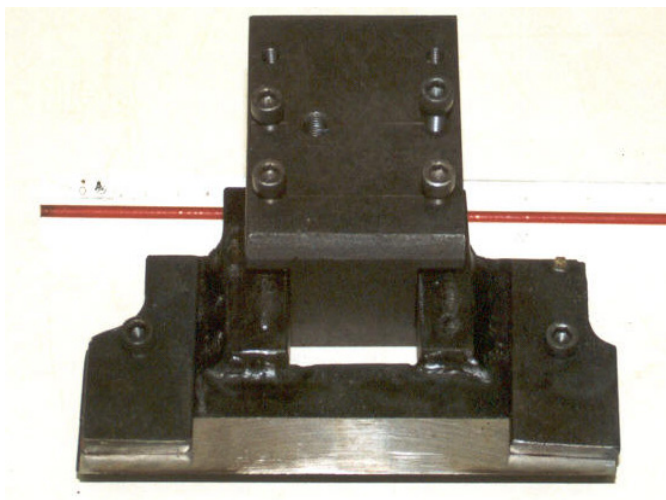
Suporte da ferramenta de corte do tipo faca
